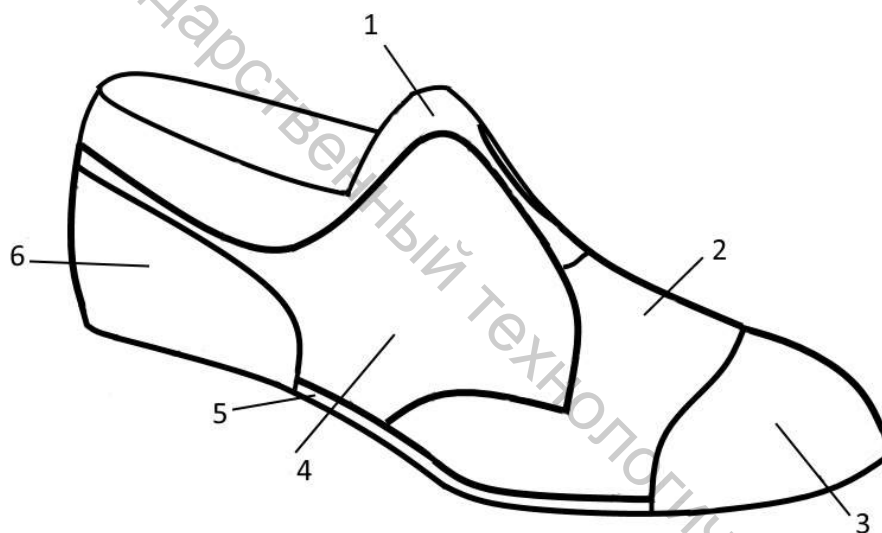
«Одетая» колодка: колодка с прикрепленными деталями:
